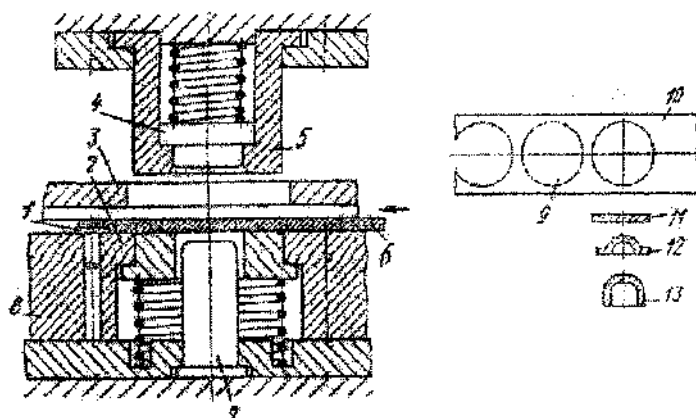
Схема штампа совмещенного действия для вырубki и вытяжки: 1 - упор; 2 - прижим; 3 - съемник; 4 - выталкиватель; 5 - пуансон вырубki и матрица вытяжки; 6 - исходная листовая заготовка; 7 - пуансон вытяжки; 9 - отход; 10 - полоса; 11 -вырубленная заготовка; 12 - начало вытяжки, 13 - изделие
